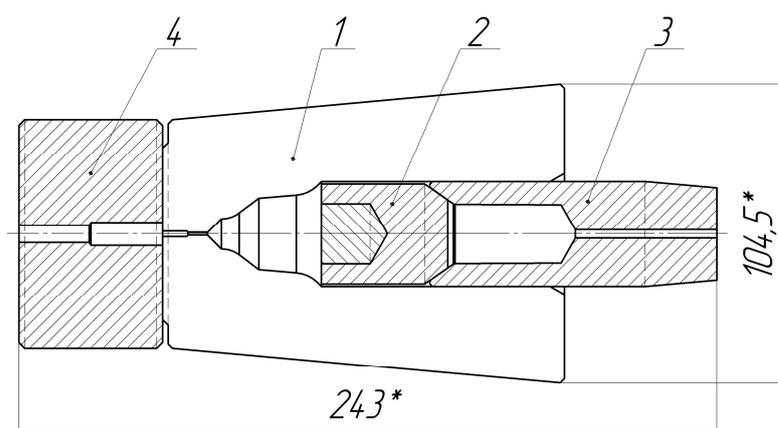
Внешний вид экспериментальной оснастки для изготовления резцов
